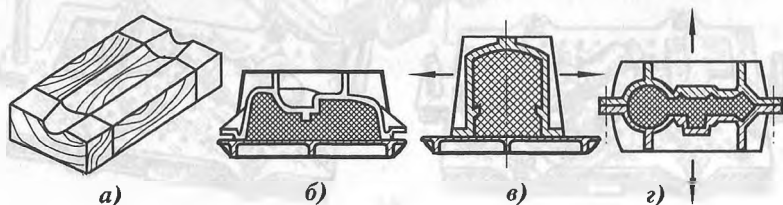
Стержневые ящики: а — деревянный (половина); металлические: б — неразъемный; в — с вертикальным разъемом; г — с горизонтальным разъемом
